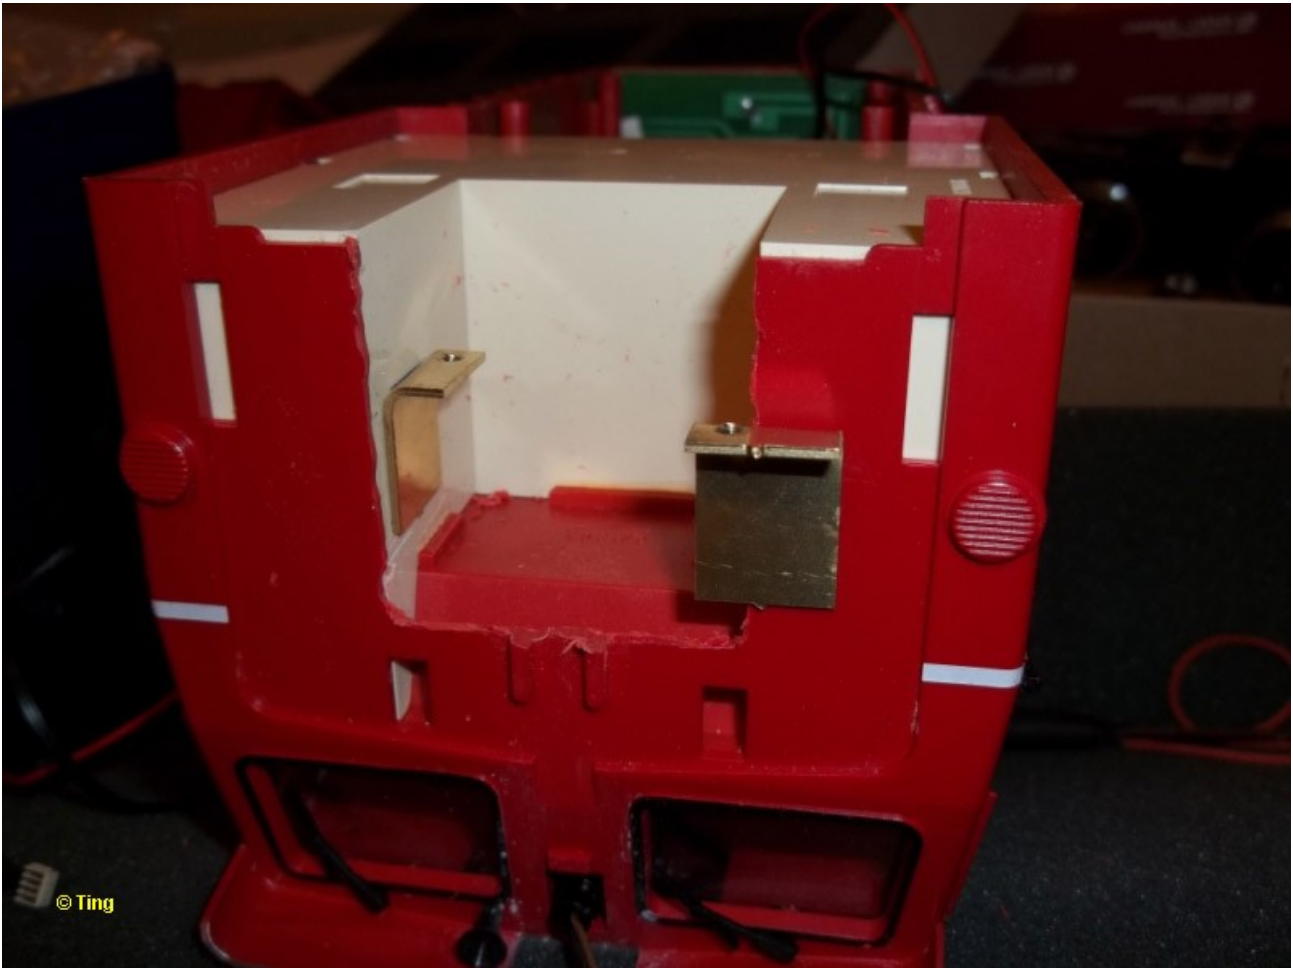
Ausfräsung Führerhaus und Befestigungswinkel.
